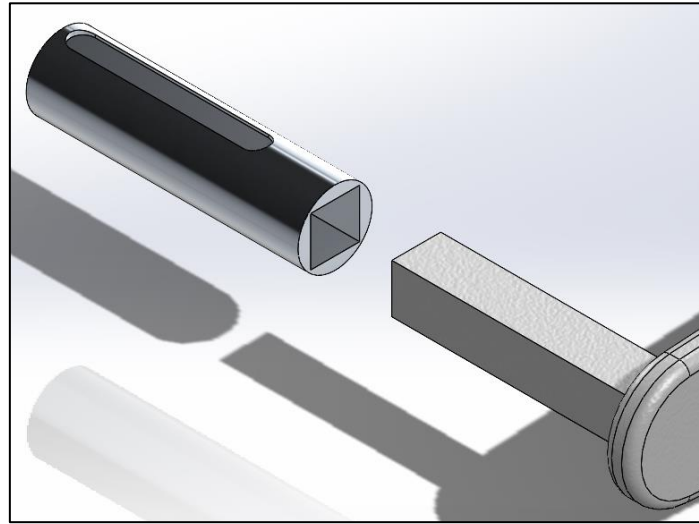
Ensamble manivela-eje del engranaje cónico. Fuente propia.
